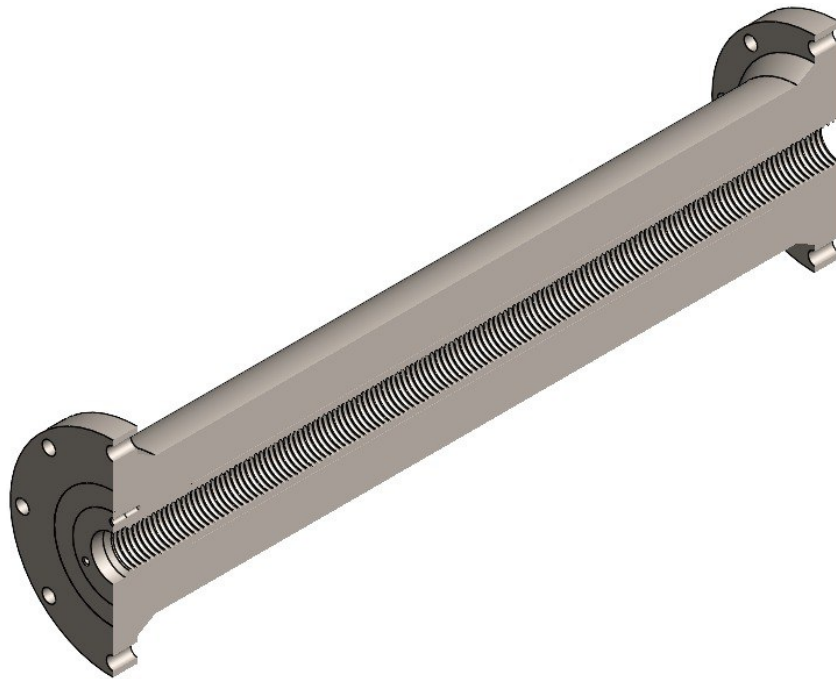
Модель модернізованої конструкції корпусу у розрізі
